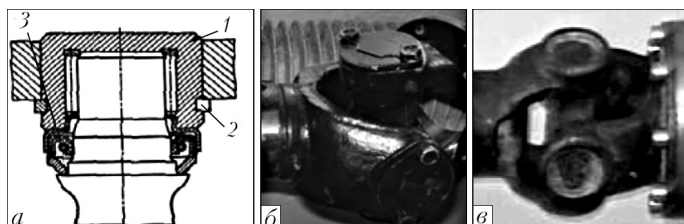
Способы фиксации стаканчика подшипника карданного шарнира: а — при помощи стопорных колец; б — при помощи болтов; в — способом кернения
